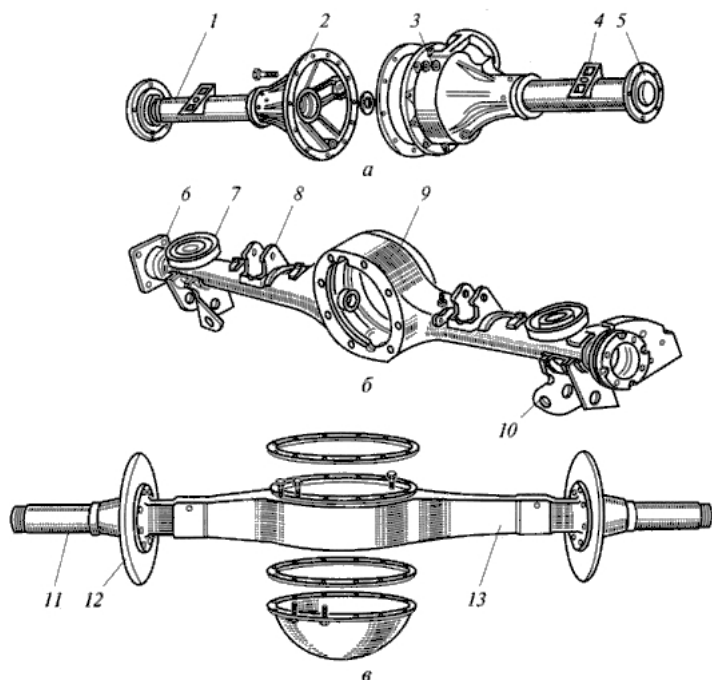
Балки ведущих мостов: *а* — разъемная балка; *б* — литая неразъемная; *в* — штампованная сварная неразъемная; 1 — кожух; 2, 3 — две половины балки; 4 — площадки крепления рессор; 5, 6, 12 — фланцы крепления опорных щитов тормозов; 7 — чашка пружины подвески; 8, 10 — кронштейны крепления продольных рычагов подвески; 9, 13 — балки; 11 — труба (полуосевой рукав)
